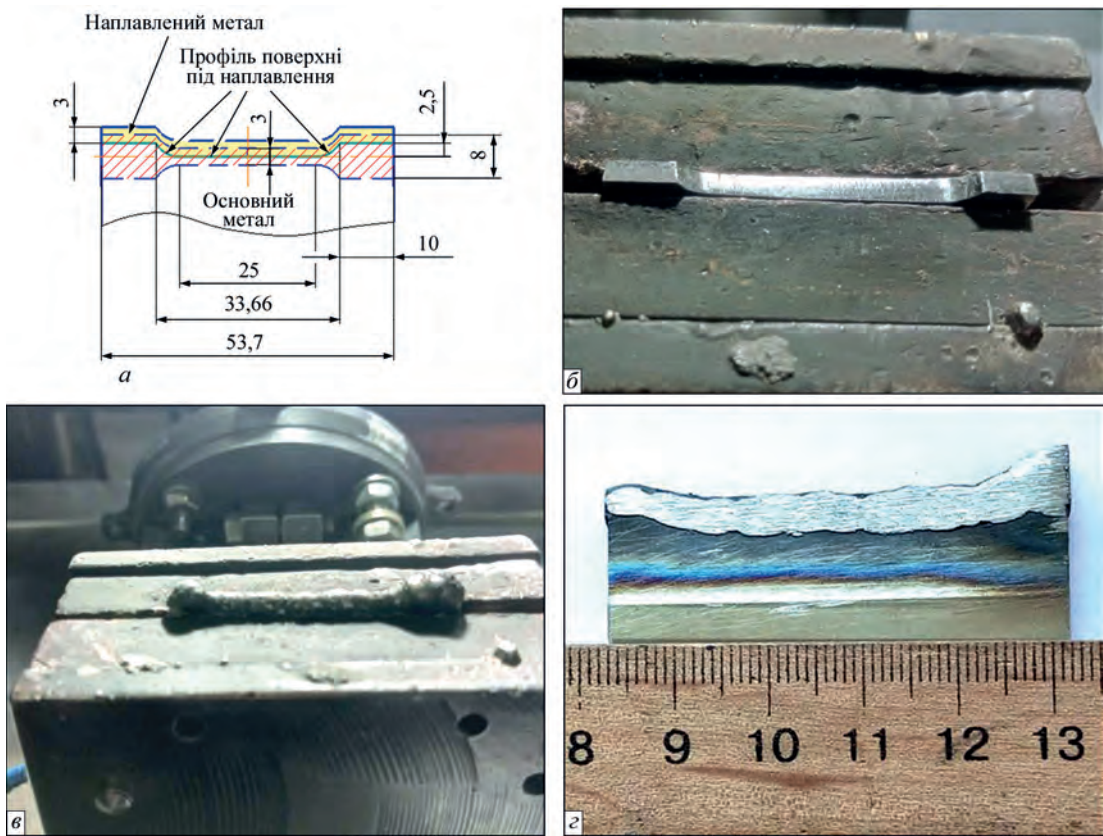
Особливості підготовки поверхні та техніки наплавлення зварної заготовки для зварного з'єднання «50 % основного + 50 % наплавленого металу» НЖС: а – схема підготовки зварної заготовки та вирізки зразка для механічних випробувань; б – попереднє формування западини перед наплавленням; в – зовнішній вид одношарового наплавлення; г – зварна заготовка після часткового видалення бокових підсилень наплавленого валика
